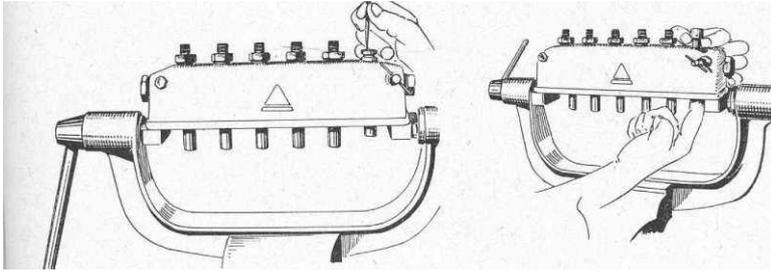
Das Saugventil wird mit einem Gewindestift herausgezogen (links) und die Kolbenführung mit einem Finger herausgeschoben (rechts)
